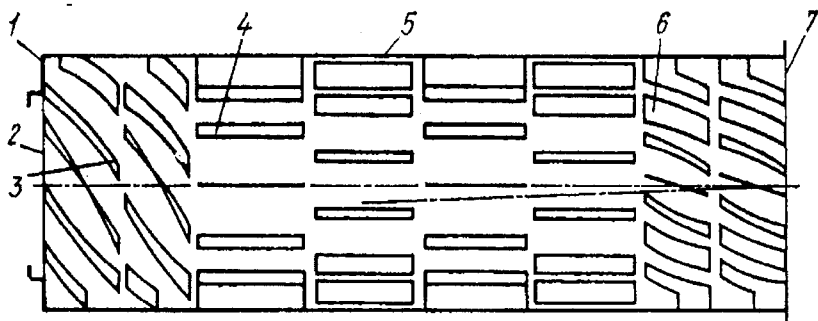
Сушильный барабан: 1 – загрузочный торец; 2 – отверстие выхода дымовых газов; 3 – отгребающие лопасти; 4 – подъемно-сбрасывающие лопасти; 5 – обечайка барабана; 6 – разгрузочные лопасти; 7 – отверстие выхода материала.
